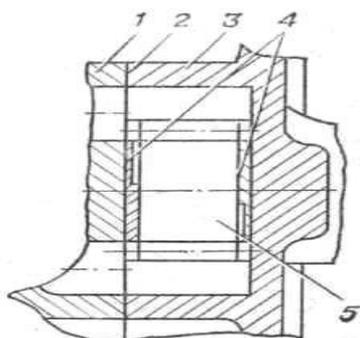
Совмещение фрезеровок в прокладках с фрезеровками в корпусе и отверстиями в крышке (обозначение позиций см. на рис. 63)
